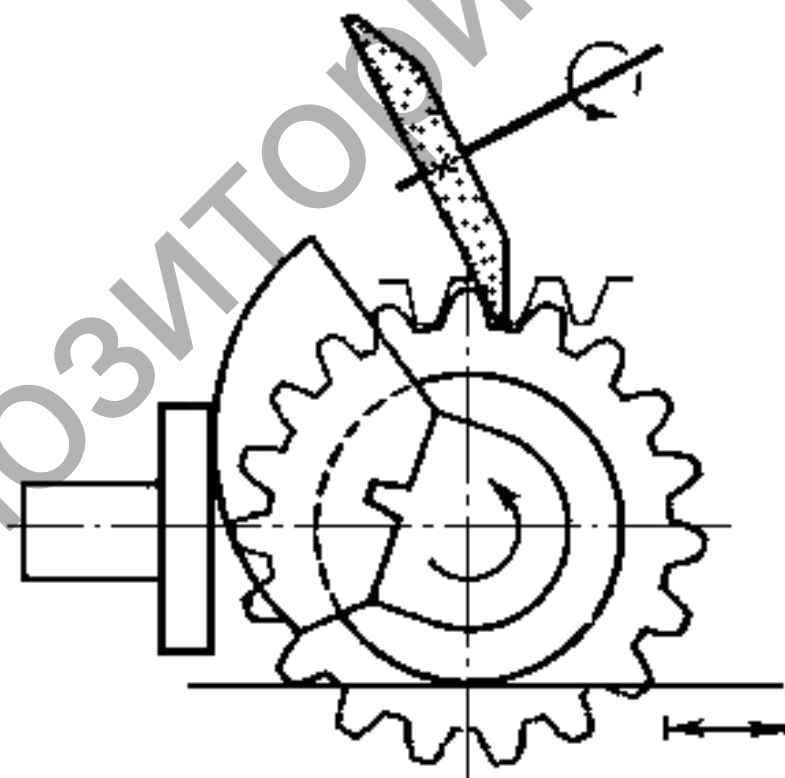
Схема шлифования зубчатых колес плоским кругом
